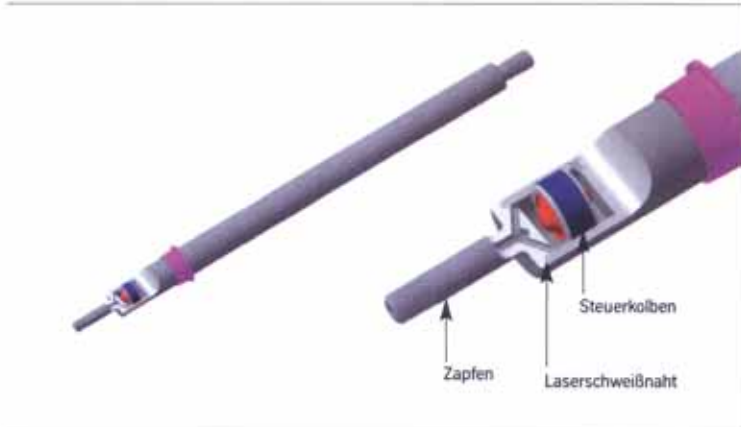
| Details der DampMatic-Kolbenstange mit Steuerkolben und Zapfen angebunden über eine Laserschweißnaht
